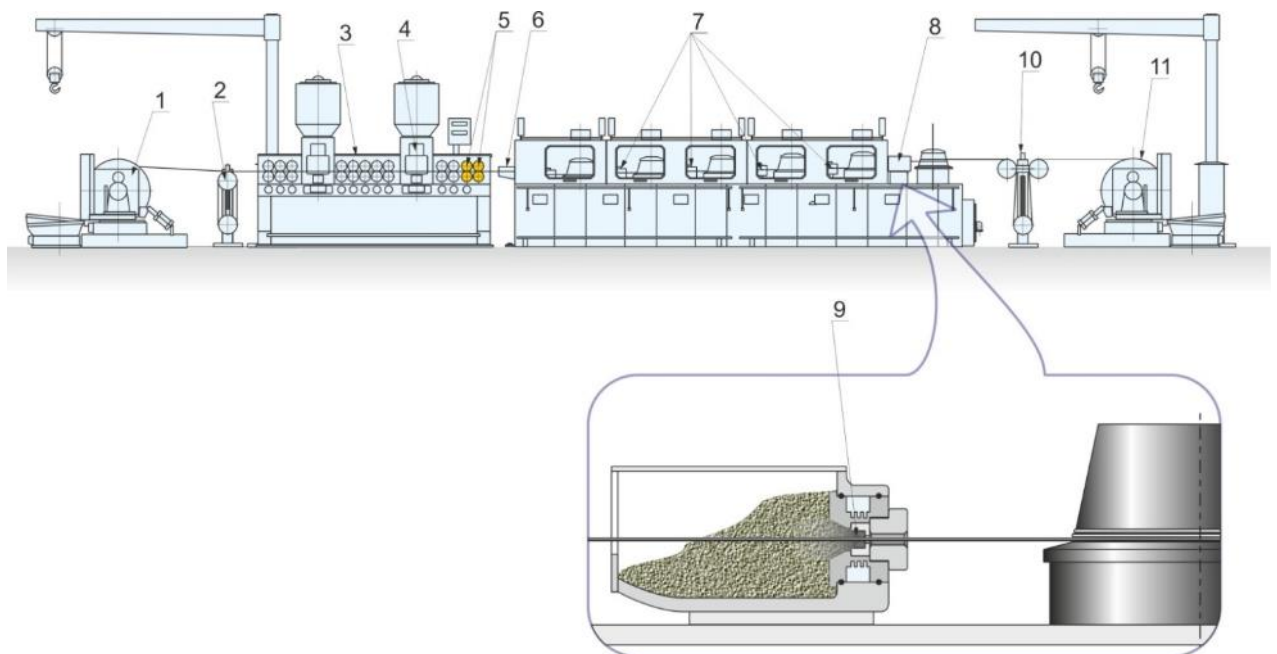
Схема виготовлення порошкового дроту за удосконаленою технологією формовки і волочіння: 1 — розмотувальний пристрій для стрічки; 2 — стійка регулювання натягу та демпфірування стрічки; 3 — формуючий агрегат; 4 — дозатор шихти; 5 — група роликів для калібрування й ущільнення; 6 — блок вхідного населення мастила з волокою; 7 — блоки проміжного населення мастила з волоками; 8 — блок нанесення протекторного покриття з калібрувальною волокою; 9 — зона утворення захисної плівки; 10 — демпфер-регулятор натягу дроту; 11 — намотувальний апарат.
